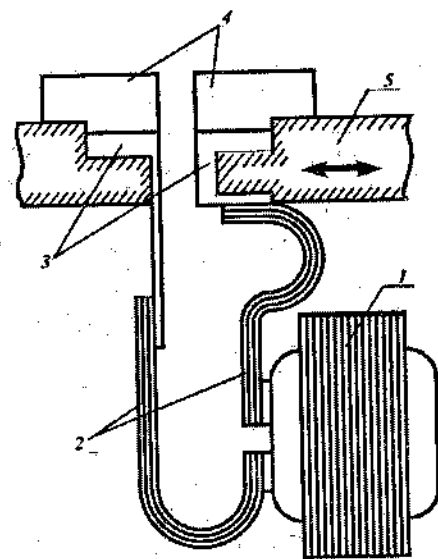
Сварочный контур машины стыковой сварки
